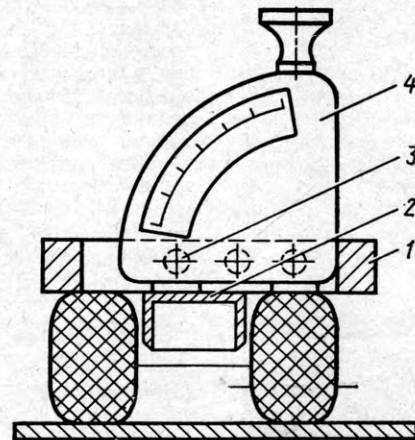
Приспособление для измерения твердости резиновых втулок с закругленными торцами: 1 — ограничительная рамка; 2 — калиброванная опорная вставка; 3 — прижимные винты; 4 — твердомер ТМ-2
